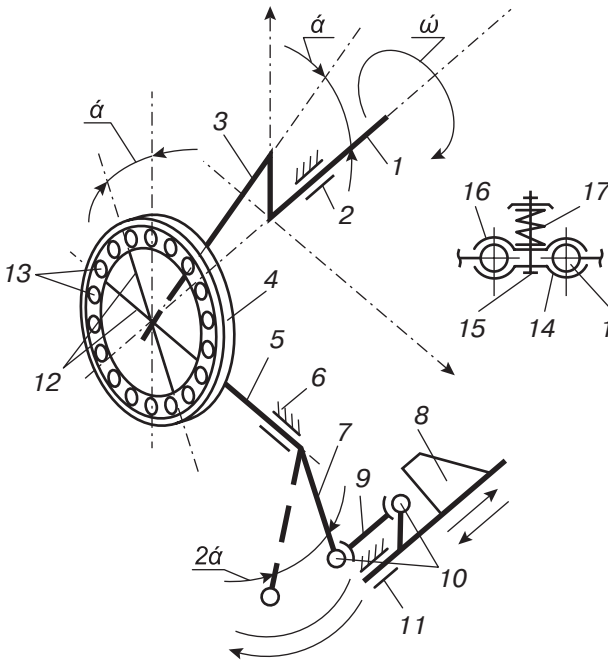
Принципова схема механізму коливальної шайби:
